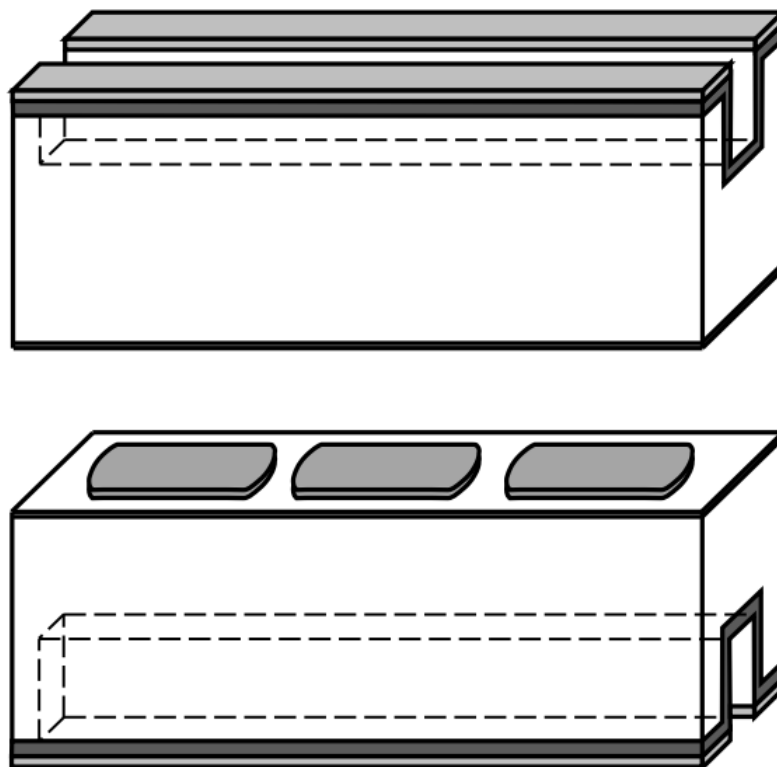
Внешний вид конструкции линейки (3 диода)
